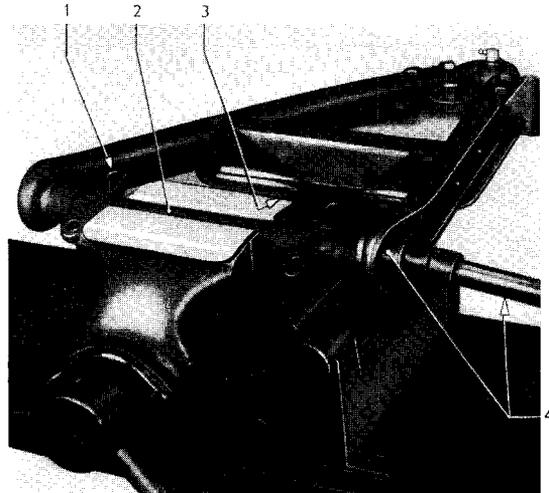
Gewindebuchse auf festen Sitz prüfen
